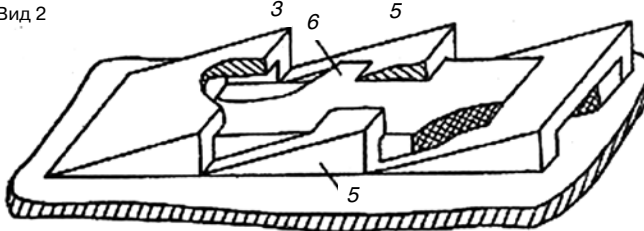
Ковш «РЕДАН»: 1 – корпус; 2 – боковые стенки; 3 – днище; 4 – режущий козырек; 5 – клиновидные накладки; 6 – защитные элементы
